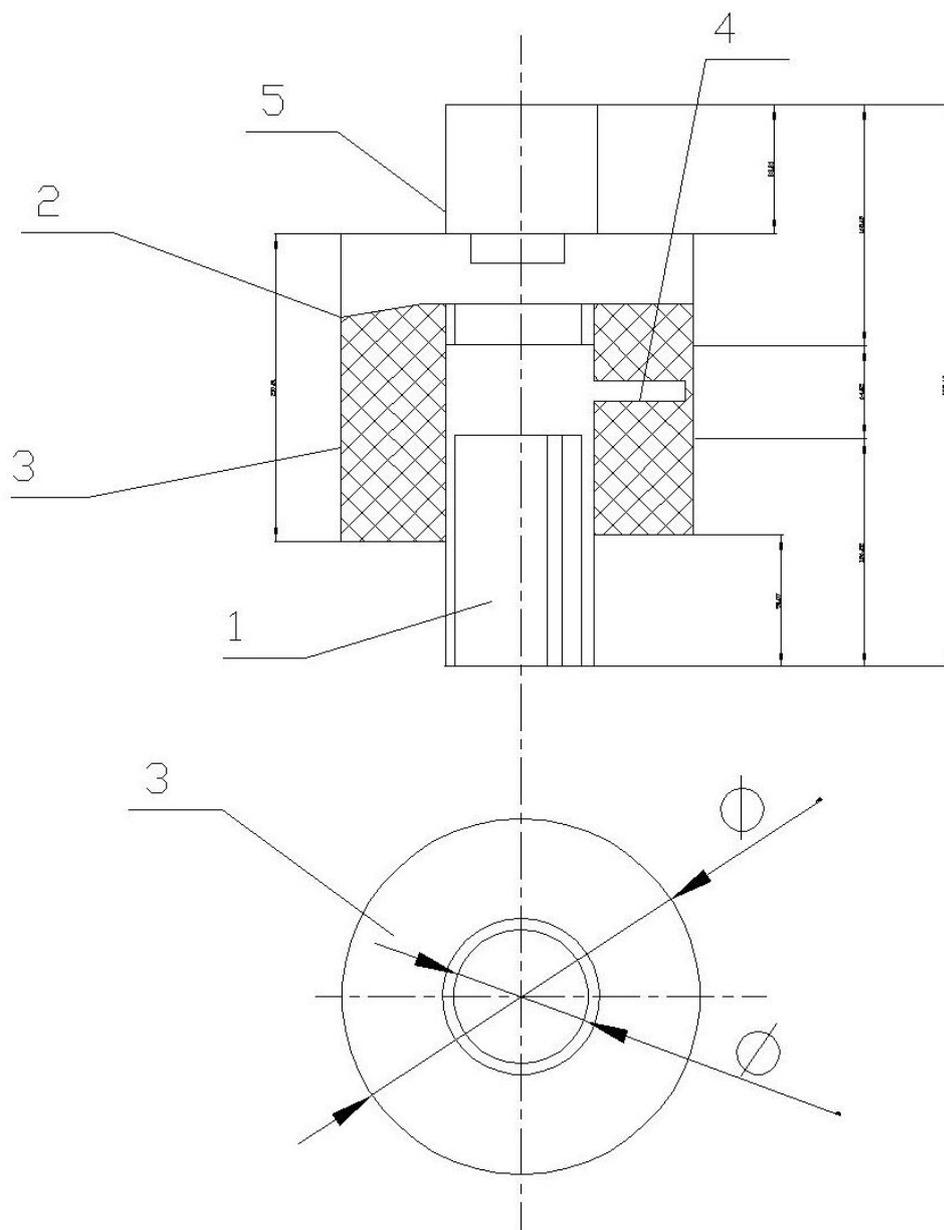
Конструкция термитного патрона для сварки
